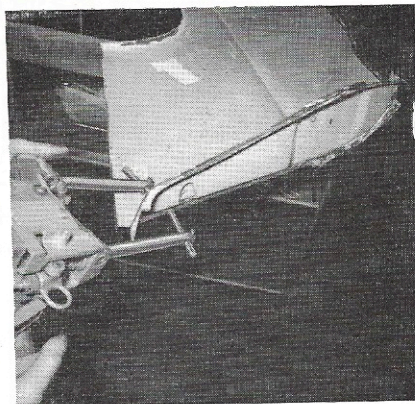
Soudage du pied d'entrée sur aile arrière. Pince ARO - porte-électrodes 253 A.
